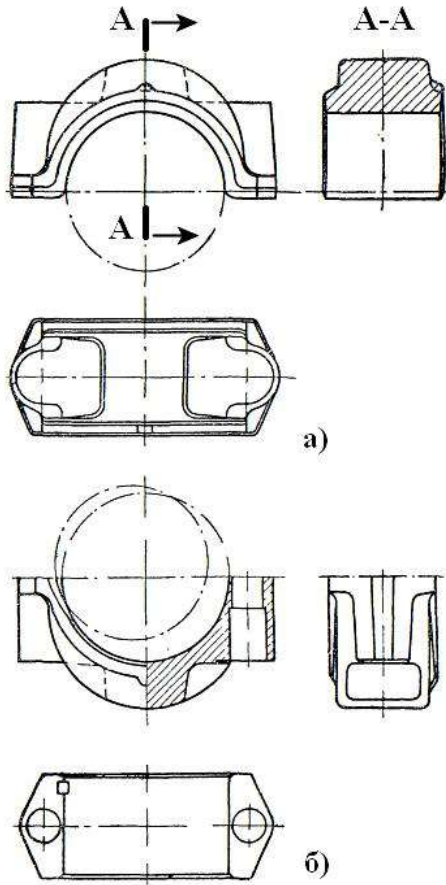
Штампована заготовка кришки (а) і готова кришка (б)
